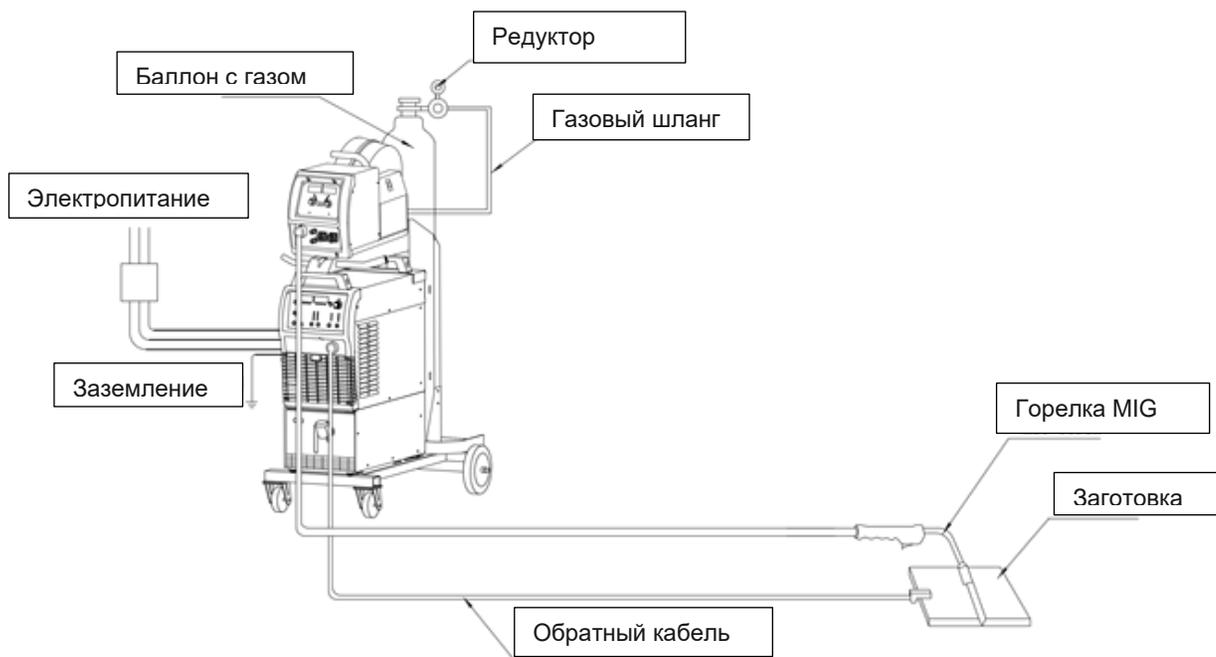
Комплект для механизированной сварки в среде защитных газов
